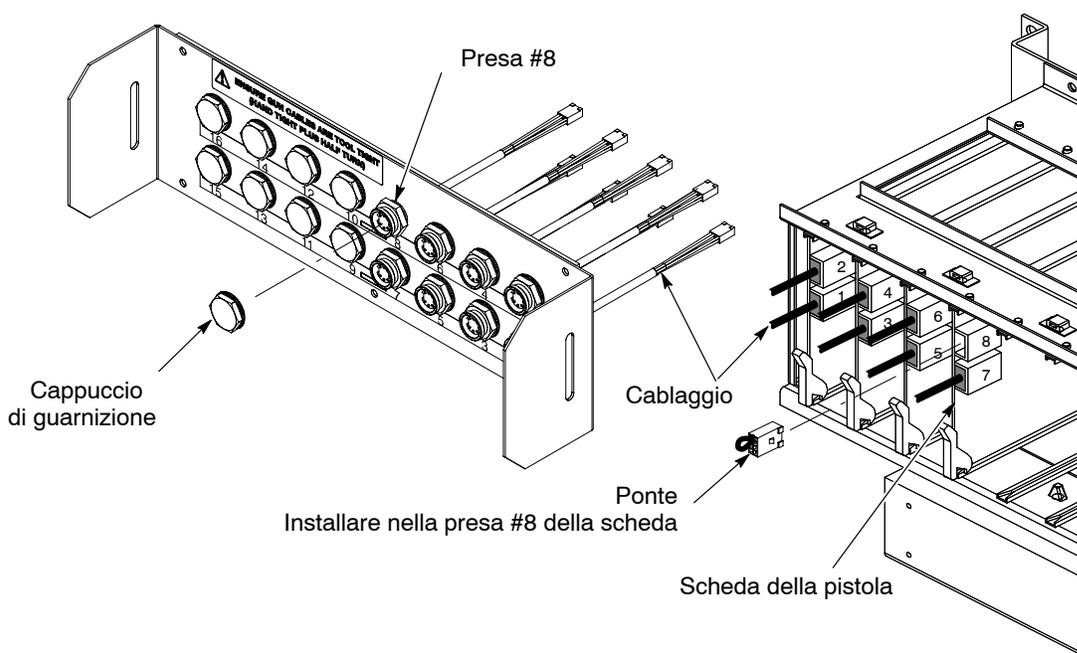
Installazione di guarnizione e ponte – Esempio di sistema da 8 pistole che impiega 7 pistole
